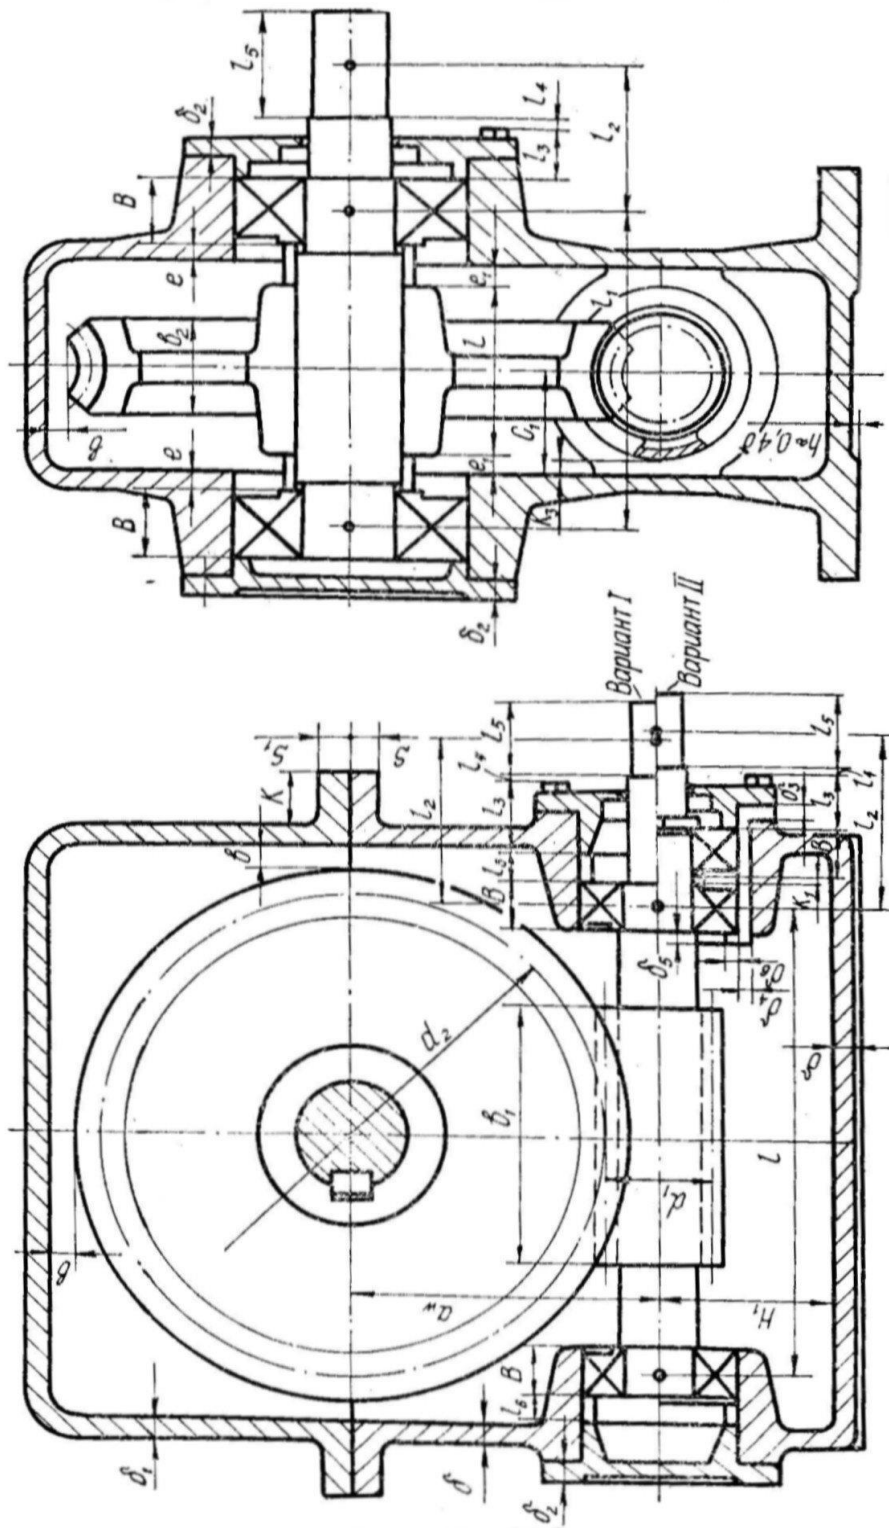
Компонувальне креслення черв'ячного редуктора
